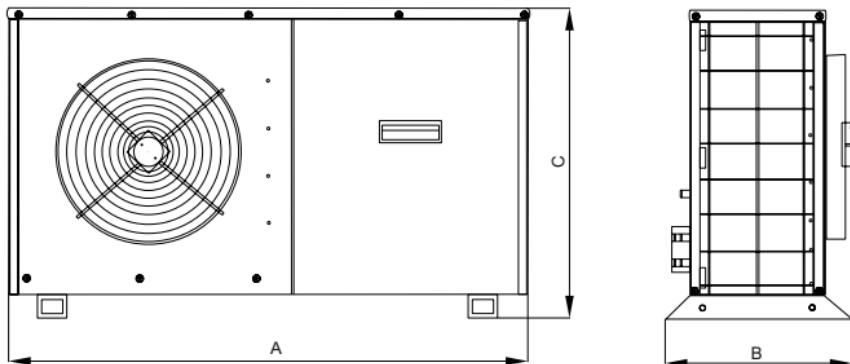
Габаритные размеры выносного конденсатора для типа AIR ROW /
